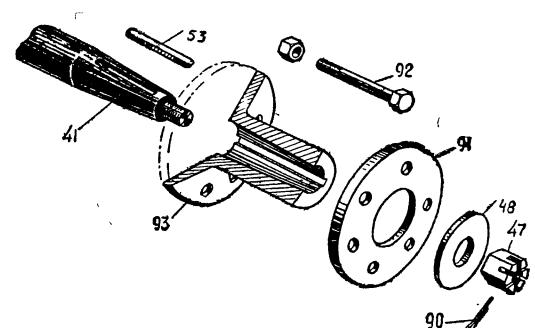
Конец вала воздушного винта с деталями для крепления винта.
